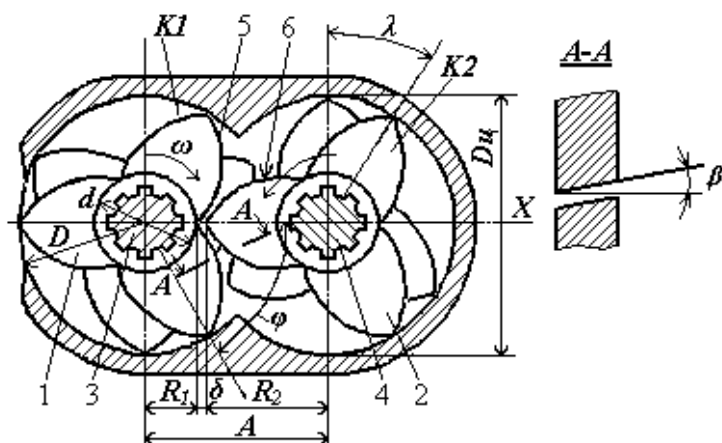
Смесительная система: 1, 2 – кулачковые колеса; 3, 4 – валы; 5, 6 – боковые поверхности
